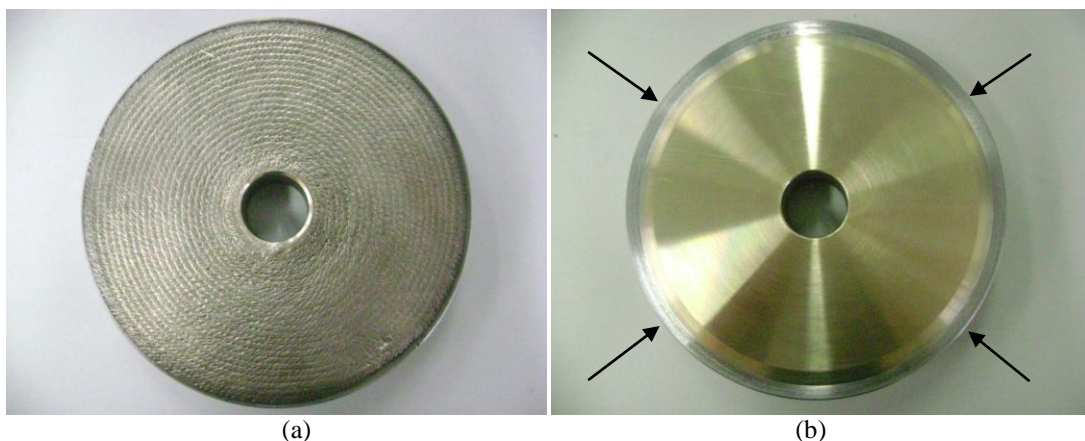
Peça de testes PT-04 na condição (a) “como soldada” e (b) usinada com setas indicando o local do revestimento
